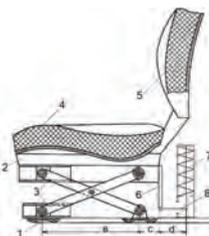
б. Общий вид подвески сиденья с направляющим механизмом типа «ножницы».
